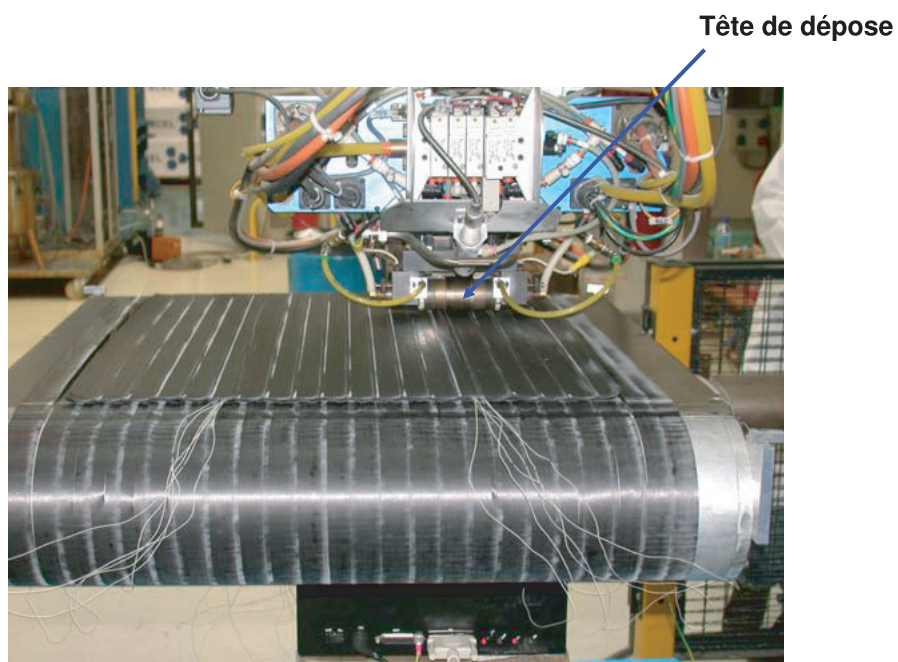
Machine en fonctionnement [Nic05]
